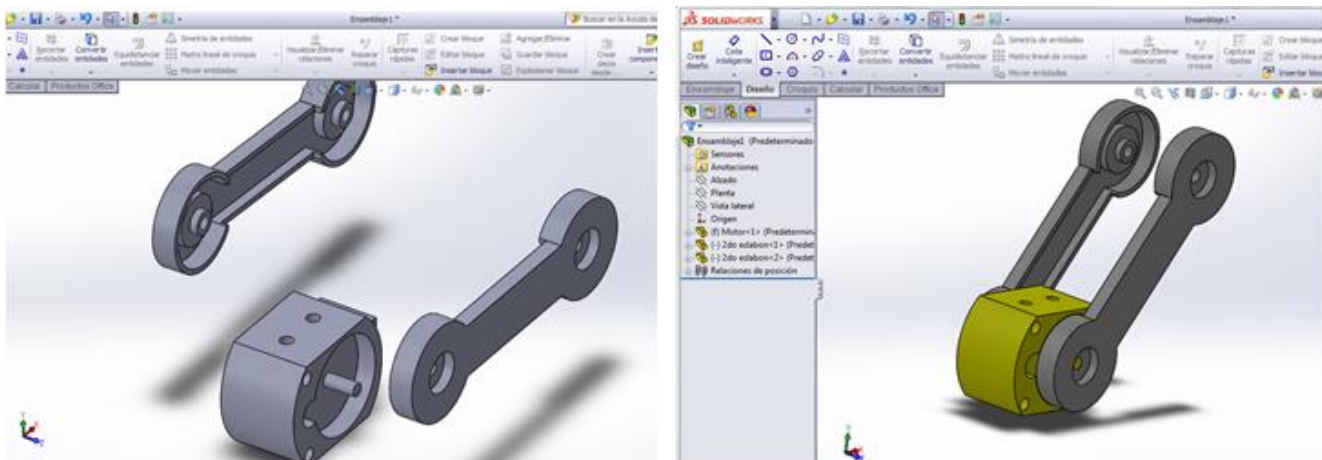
Izquierda: piezas antes del ensamble. Derecha Piezas ensambladas y adición de apariencia (Ensamble 2).
